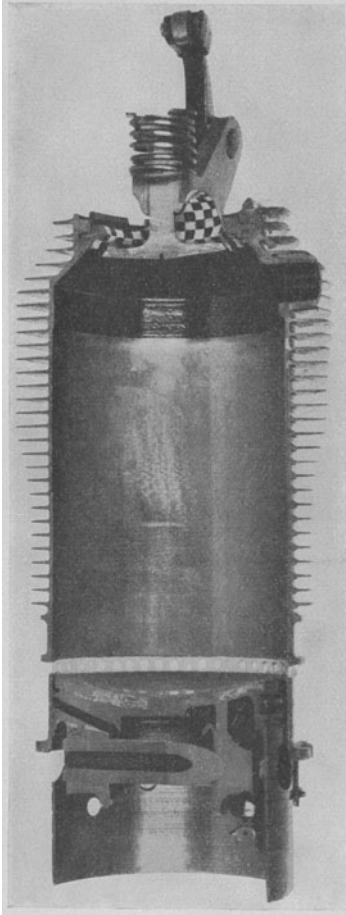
Zylinder des Ein-ventil-Gnôme-Motors.
